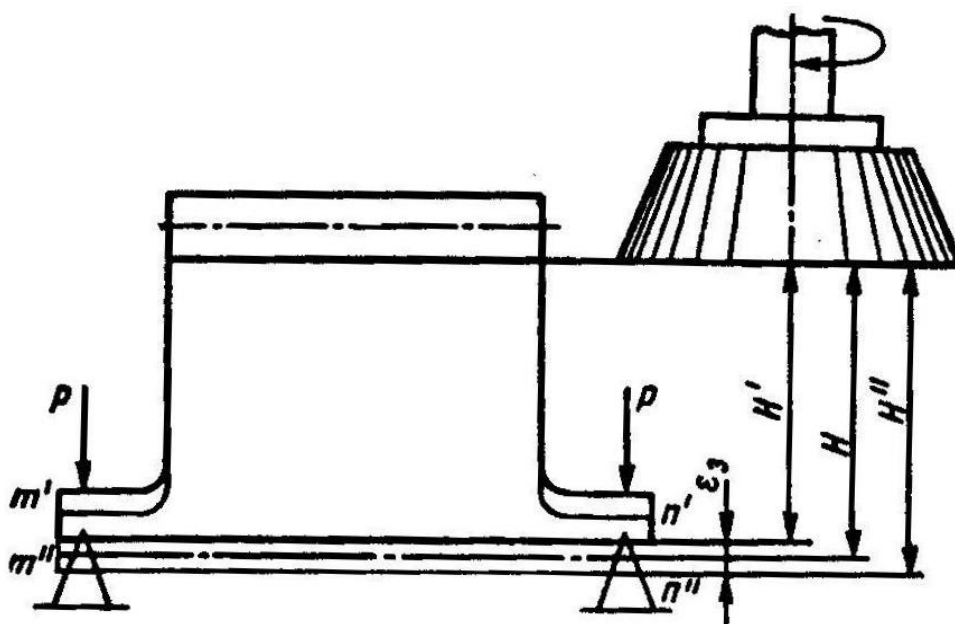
Схема осадки заготовки при закріпленні із силою P , спрямованої перпендикулярно до опорної бази
